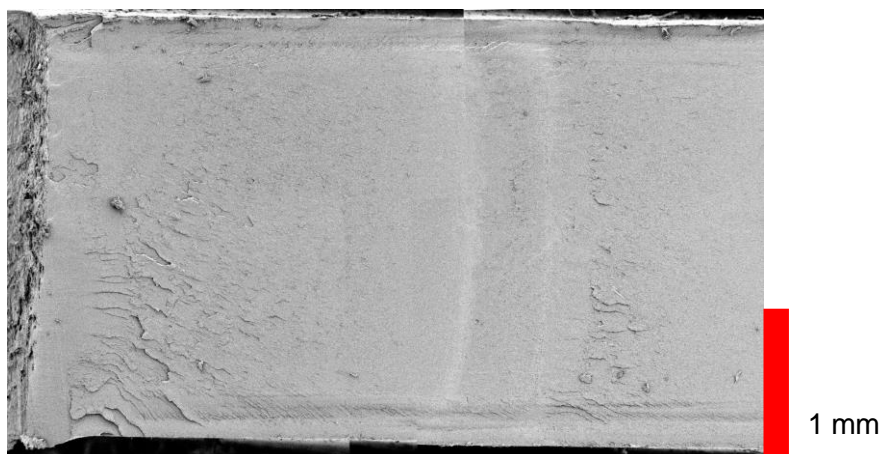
Imatge composta de la superfície de fractura de REX-PLA
